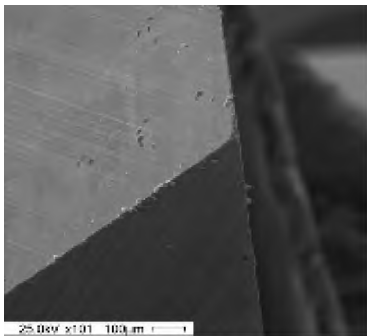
Стан ріжучої крайки інструмента після заточування
